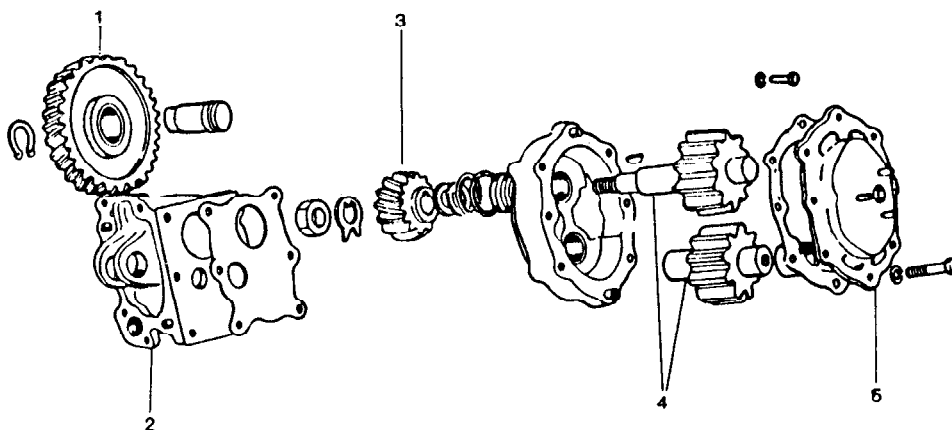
Piezas de una bomba de aceite impulsada por engranes: 1 engrane intermedio, 2 cuerpo para engrane intermedio, 3 engrane de mando, 4 engranes de la bomba, 5 tapa
